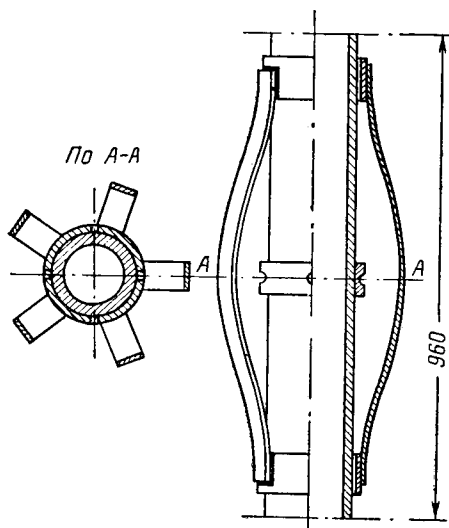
Центрирующий пружинный фонарь ГрозНИИ.
